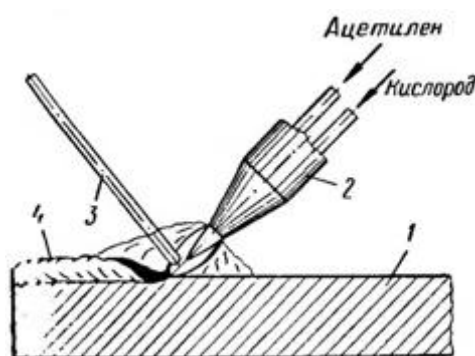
Схема газовой наплавки: 1 – наплаваемая деталь; 2 – газовая горелка; 3 – присадочный материал; 4 – наплавленный металл
